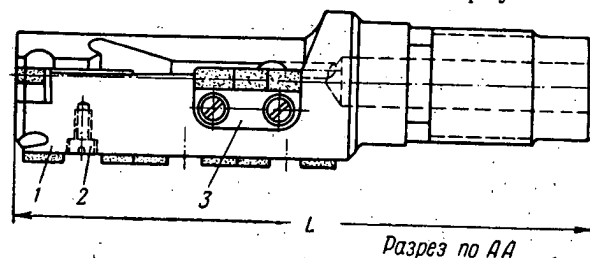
Схема наладки токарного станка для скоростного развертывания цилиндров.
